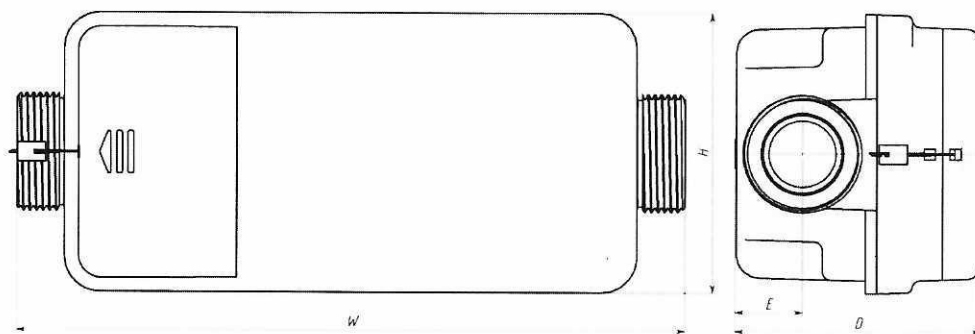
Габаритные и присоединительные размеры Модели 2 и 3
